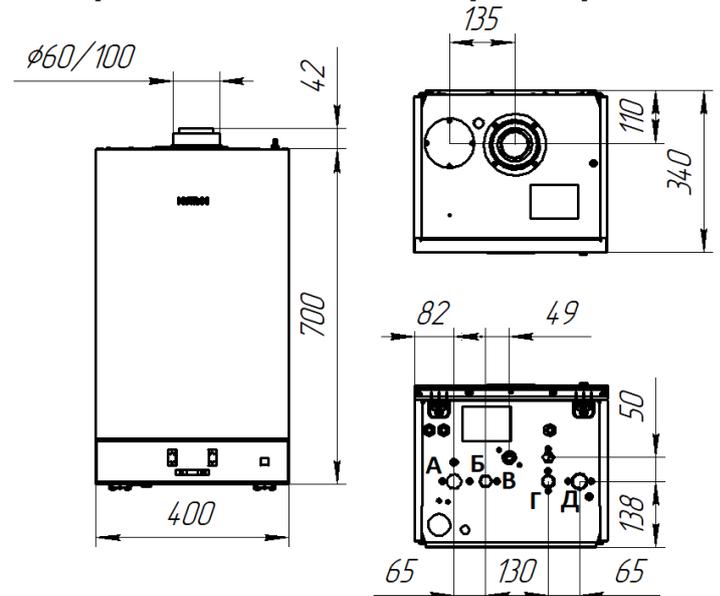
Габаритные и присоединительные размеры PC35-00.00.
